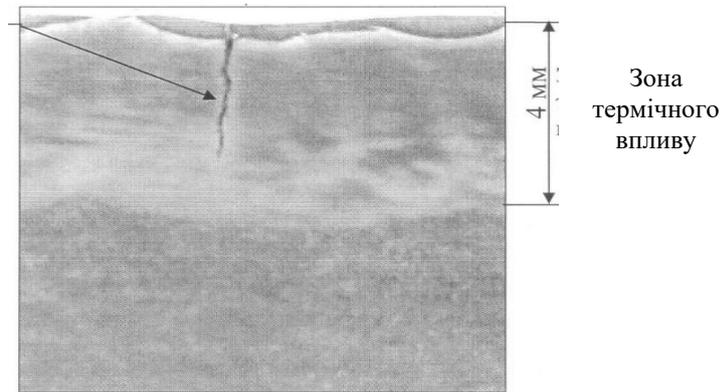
Макроструктура зразка поперечного перерізу робочої втулки
